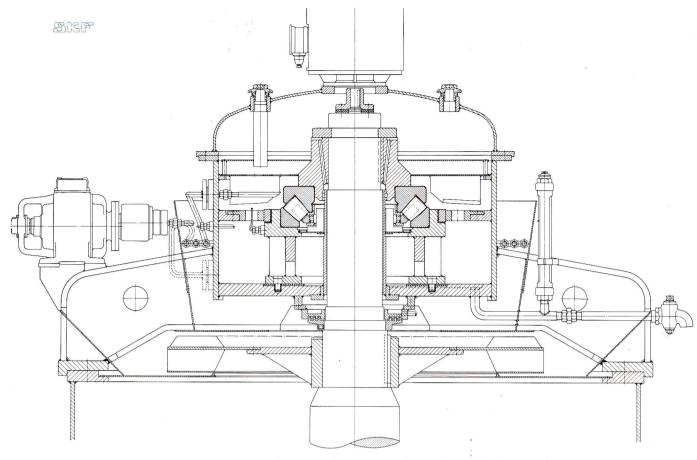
El cojinete de suspensión para generador y turbina hidráulica
